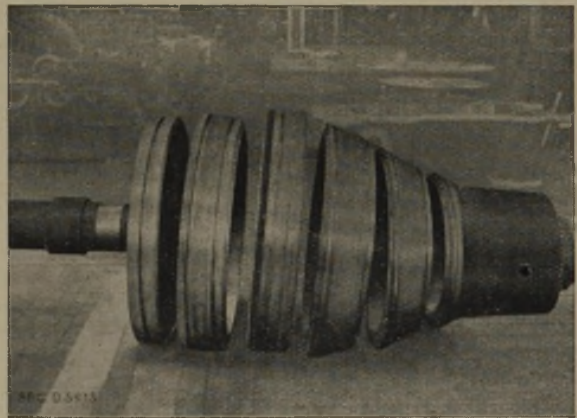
BBC-Elektroschweißung, Einzelteile einer Schweißwelle für Turbine (Werkfoto BBC)
